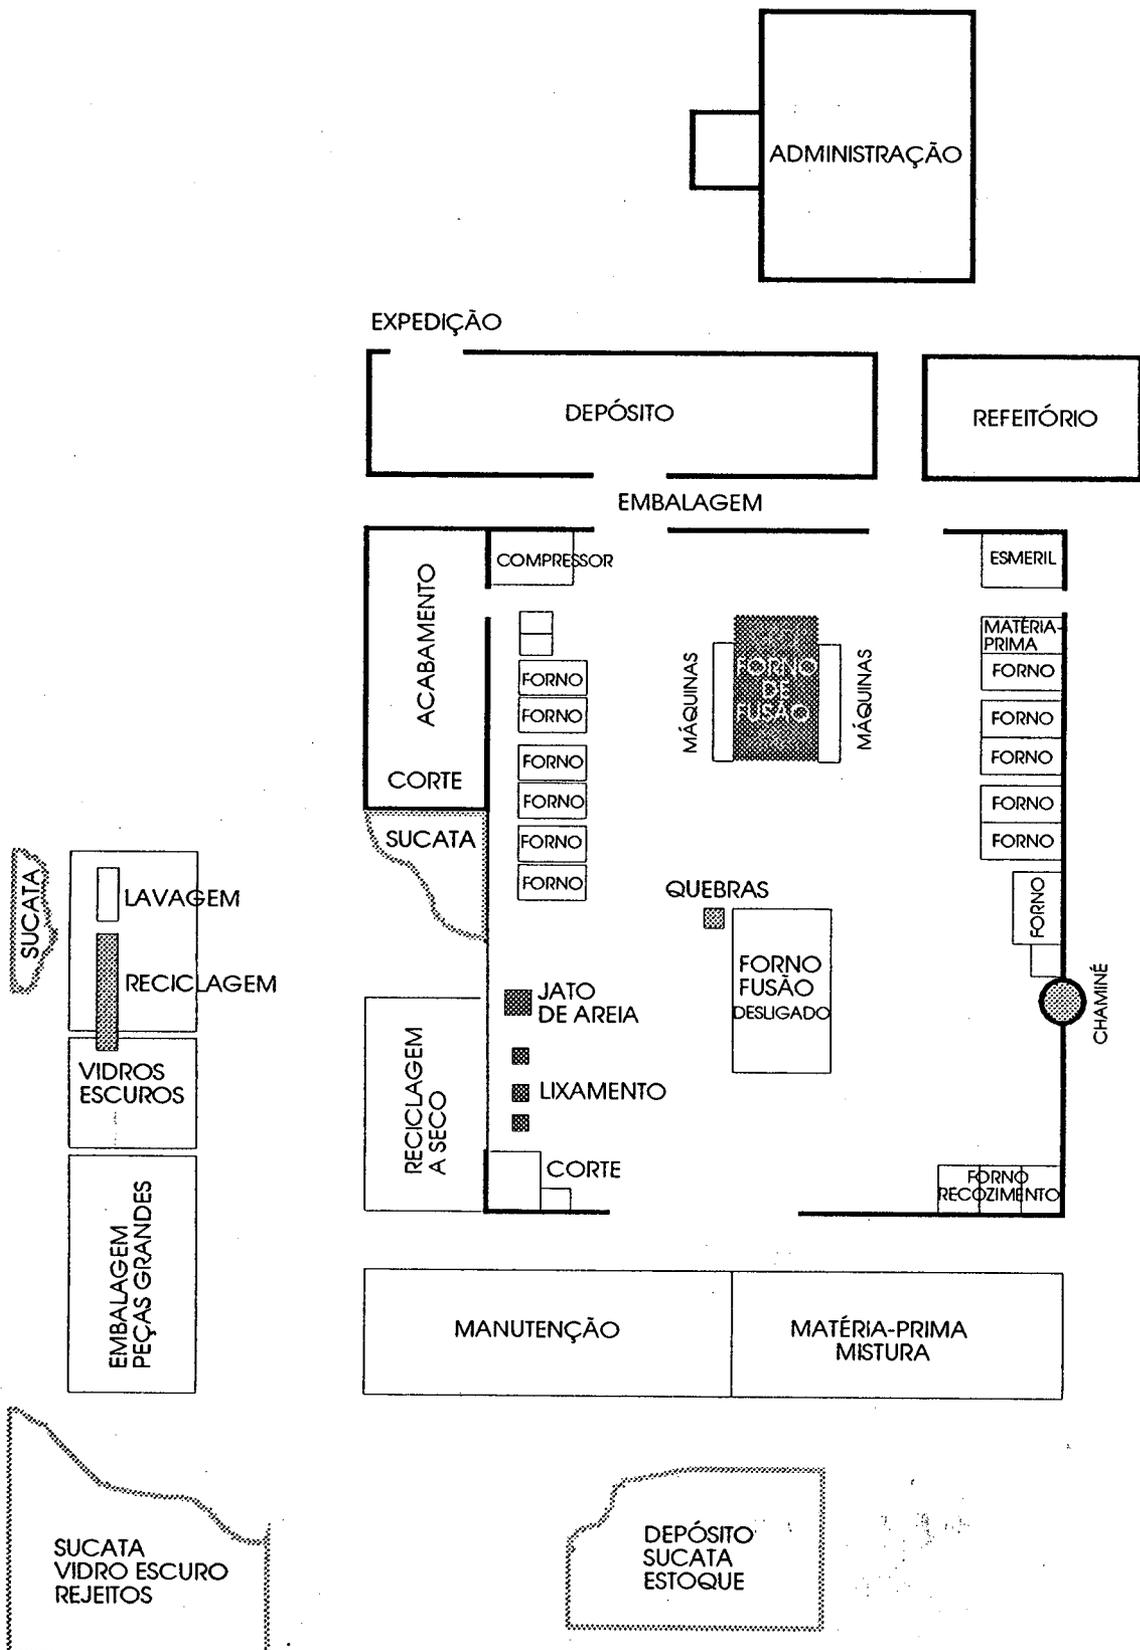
LAYOUT DO SISTEMA PRODUTIVO
